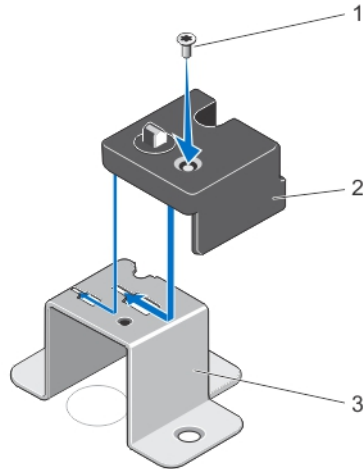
Instalación del seguro de bloqueo de la cubierta superior
